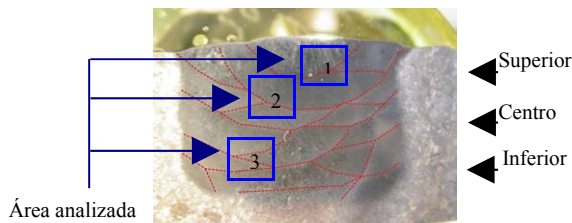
Macrografia do aço soldado segundo a temperatura de interpasse a 80°C.
